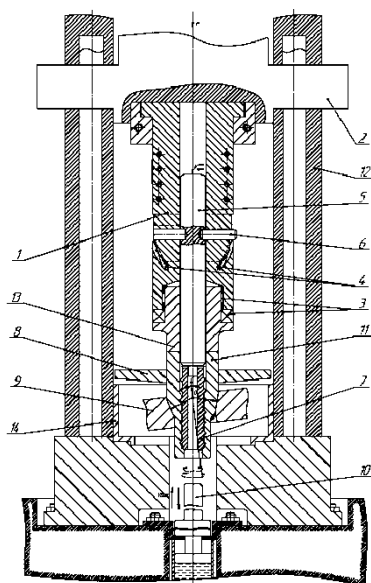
Устройство для формирования пазов в обкатывающем инструменте:
